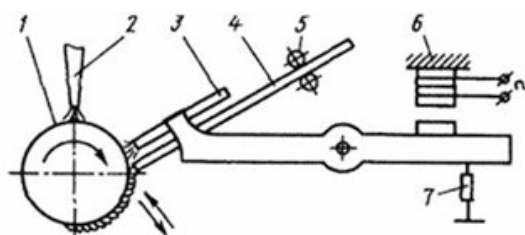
Схема вибродуговой наплавки: 1 – наплаваемое изделие; 2 – сопло для подачи, охлаждающей изделие жидкости; 3 – сопло для подачи жидкости в зону сварки; 4 – электродная проволока; 5 – подающие ролики; 6 – электромагнитный вибратор; 7 – пружина
